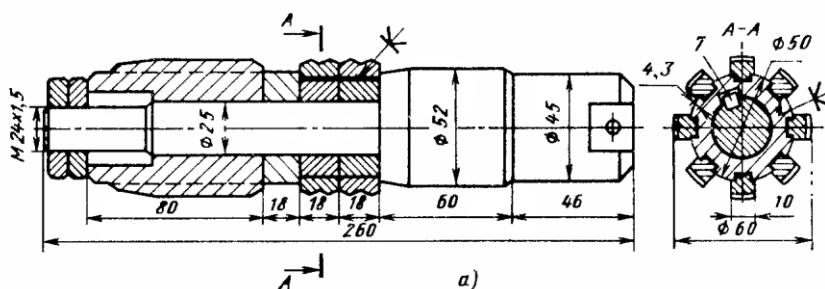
Шліцьова протяжка з вклеєними робочими елементами з твердого сплаву
